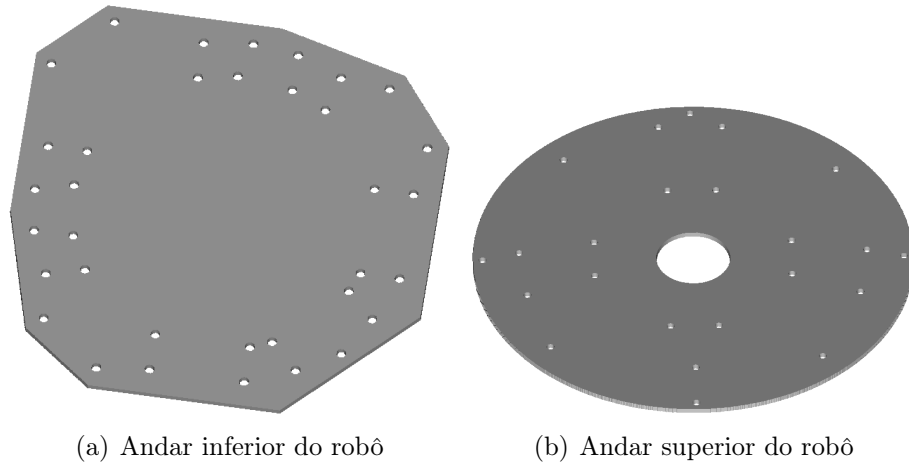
Desenhos 3D das bases de suporte do robô.
